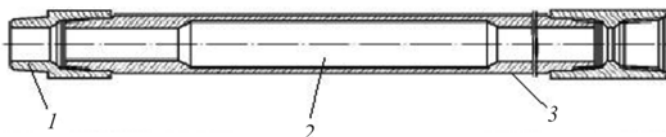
Виды аварий с бурильными трубами из легких сплавов: 1 – срыв резьбового соединения; 2 – абразивный и коррозионный износ тела трубы; 3 – повышенный износ тела трубы в интервале клинового захвата
